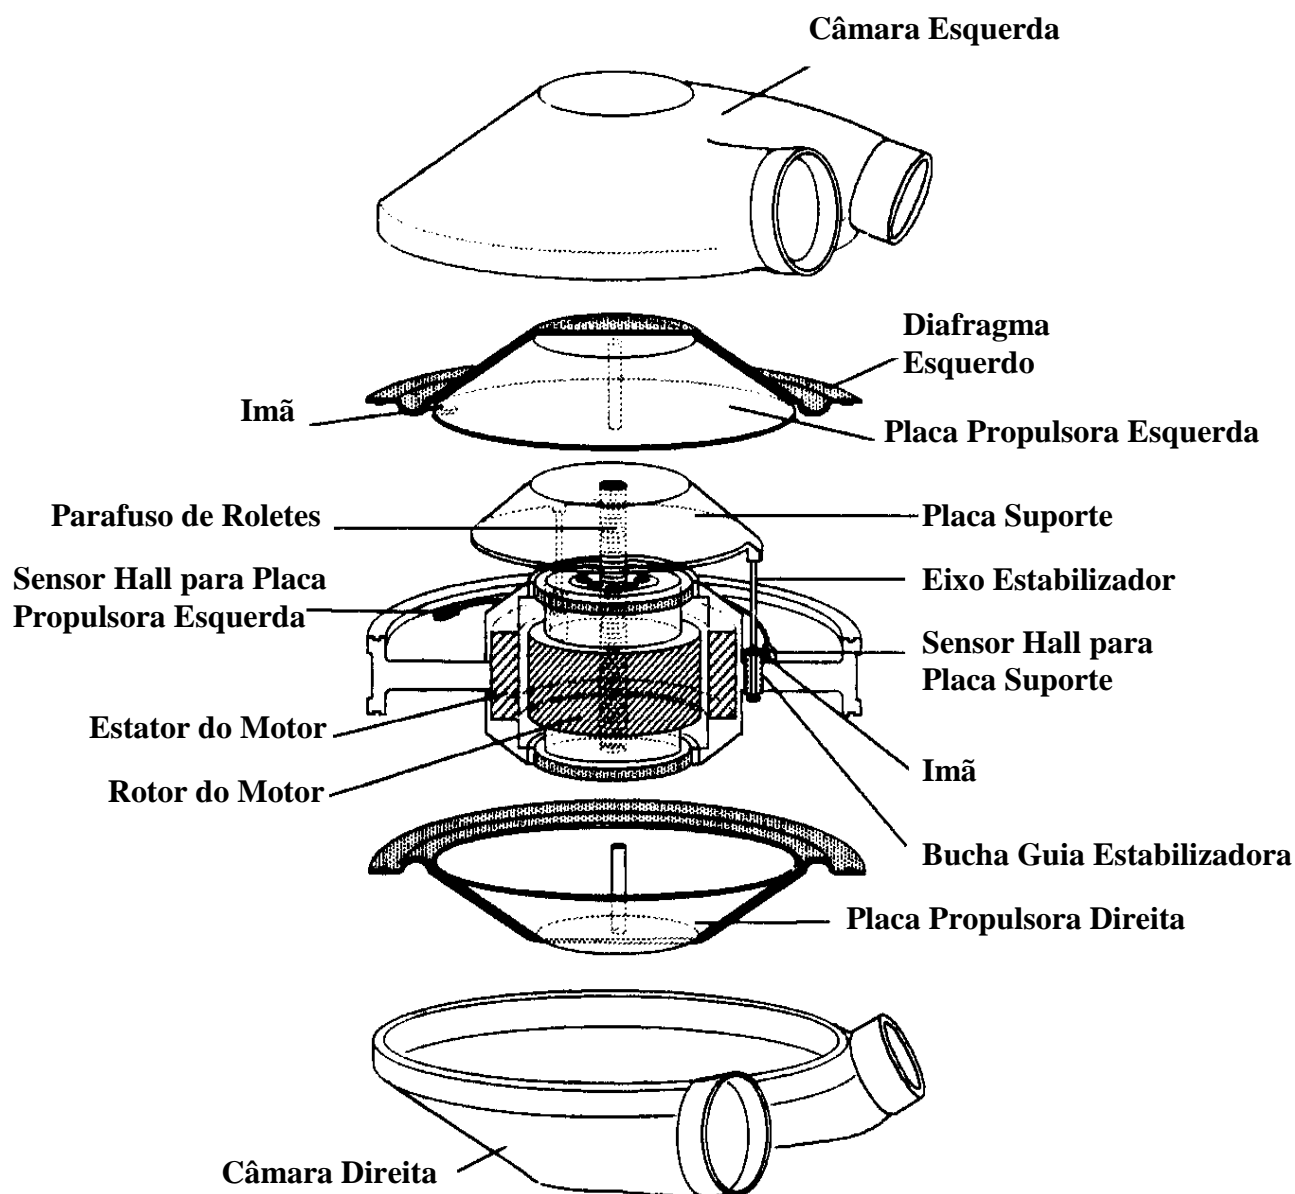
Vista explodida do CAA, mostrando seus componentes eletro-mecânicos e os sensores internos de monitoração do posicionamento do parafuso de roletes e do diafragma esquerdo.
